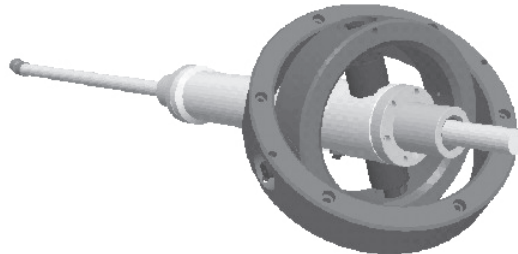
Prototyp eines lineardirektangetriebenen Aktors [INSTITUT FÜR FERTIGUNGSTECHNIK UND WERKZEUGMASCHINEN IFW DER UNIVERSITÄT HANNOVER]
